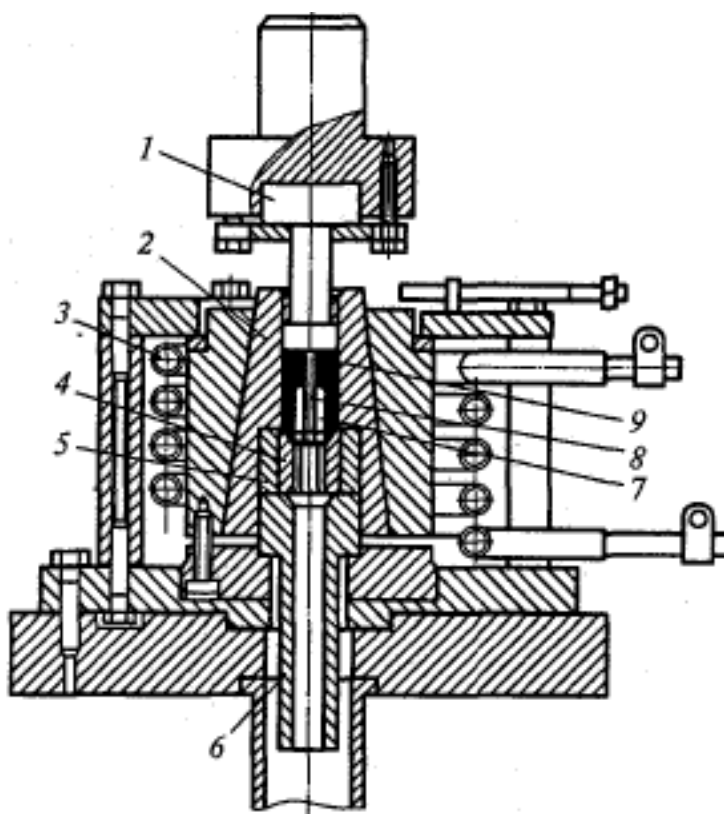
Схема типового штампа для гарячого гідродинамічного видавлювання інструмента
